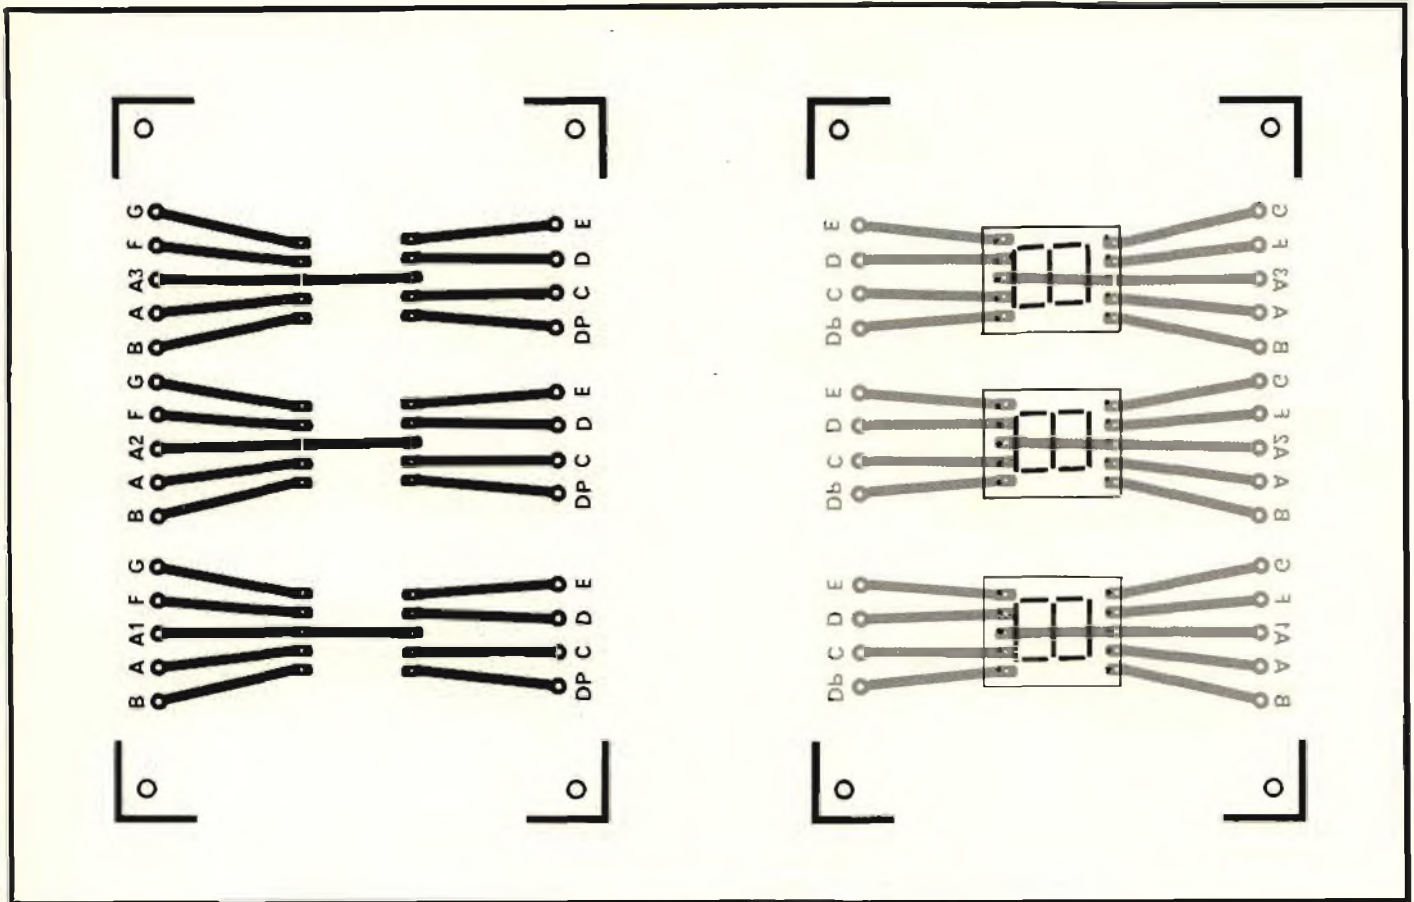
A sinistra è visibile il circuito stampato in scala 1:1 della basetta display, a destra è invece riportato il montaggio dei 3 componenti.
